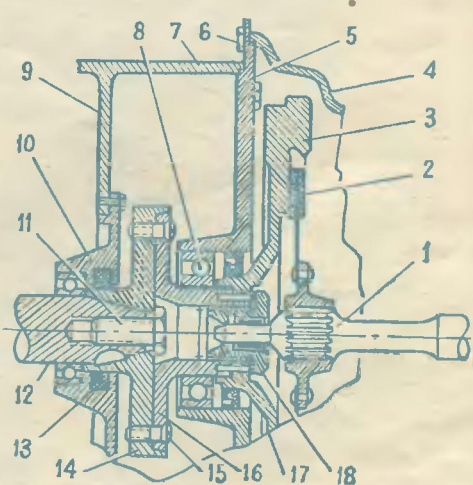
Соединение двигателя с КП: 1 — первичный вал КП; 2 — фрикционный диск сцепления; 3 — маховик; 4 — картер коробки передач; 5 — переходный фланец; 6 — болт крепления фланца к КП; 7 — корпус; 8 — подшипник №310; 9 — картер двигателя; 10 — задняя крышка двигателя; 11 — болт М10; 12 — хвостовик молотчатого вала; 13 — сайлинг; 14 — переходник; 15 — болт М8; 16 — вал маховика; 17 — штифт; 18 — болт маховика с гильзчатый подшипником.
